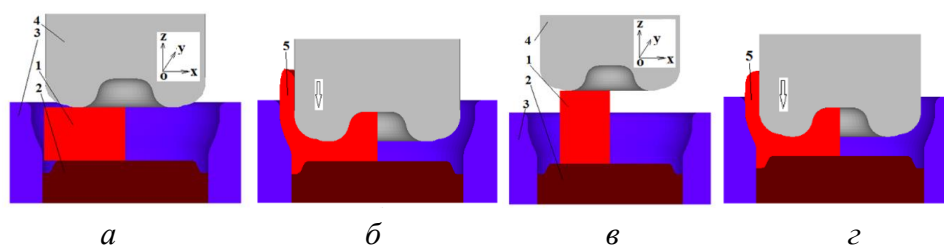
Розрахункові схеми на початку і в кінці видавлювання: а і б - заготовки круглого перерізу; в і г - заготовки квадратного перерізу
